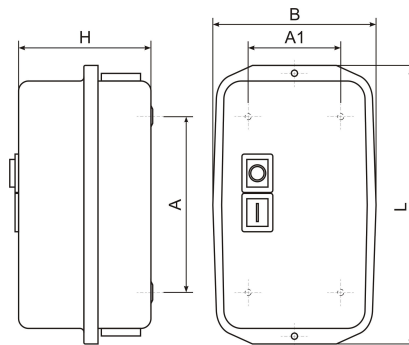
Пускатели ПМ12-040/ПМ12-063 в металлическом защитном корпусе со степенью защиты IP54.
